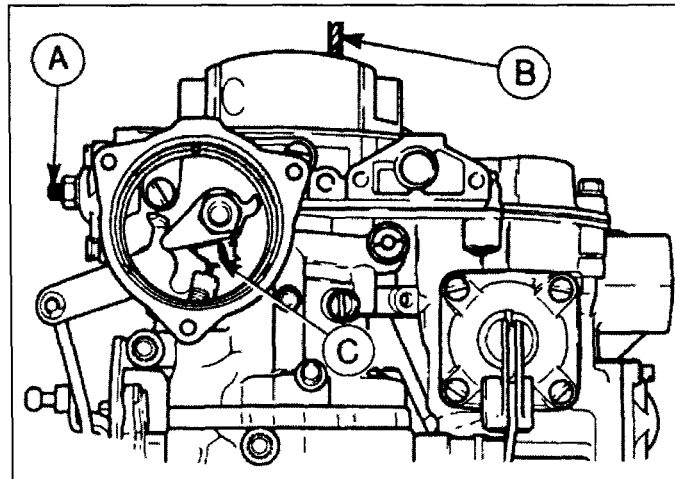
Установка карбюратора для регулировки привода пускового устройства
